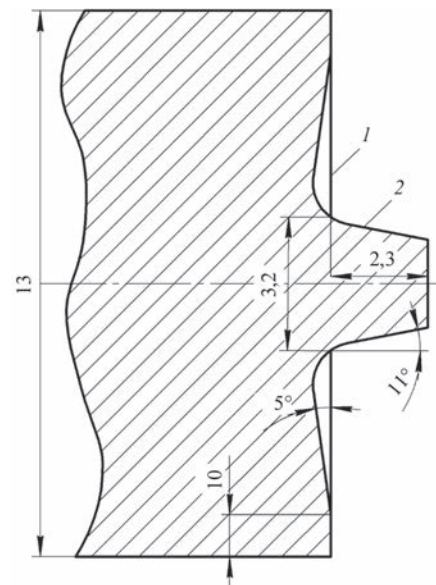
Схематичне зображення робочого інструмента для ЗТП: 1 — заплечик; 2 — штир
